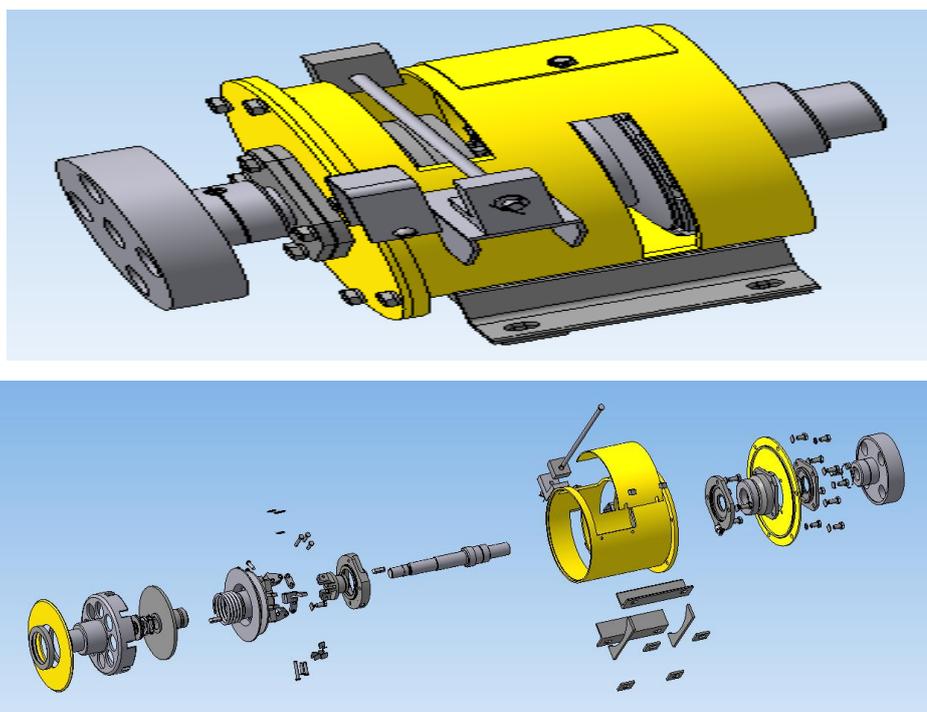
Общая сборка и разнесенная сборка муфты сцепления.
